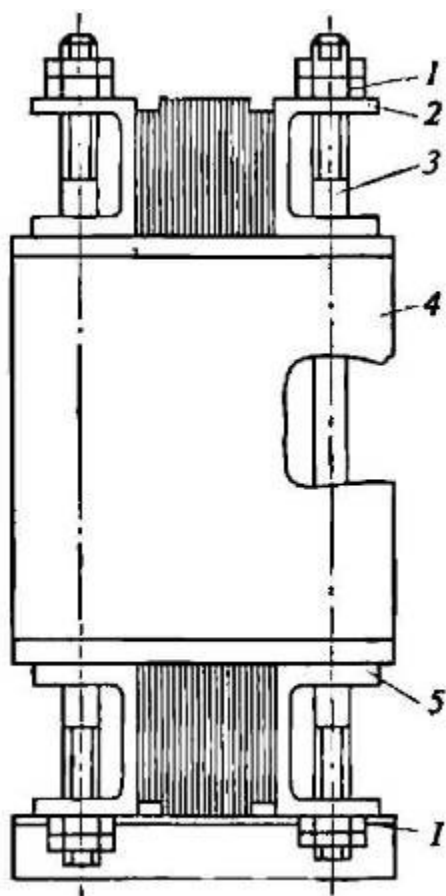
Подпрессовка обмоток трансформатора ярмовыми балками: 1 - гайки; 2 и 5 - ярмовые балки; 3 - шпильки; 4 - обмотка
